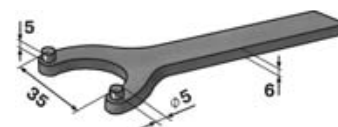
Размеры ключа для снятия гайки резервуара амортизатора.
